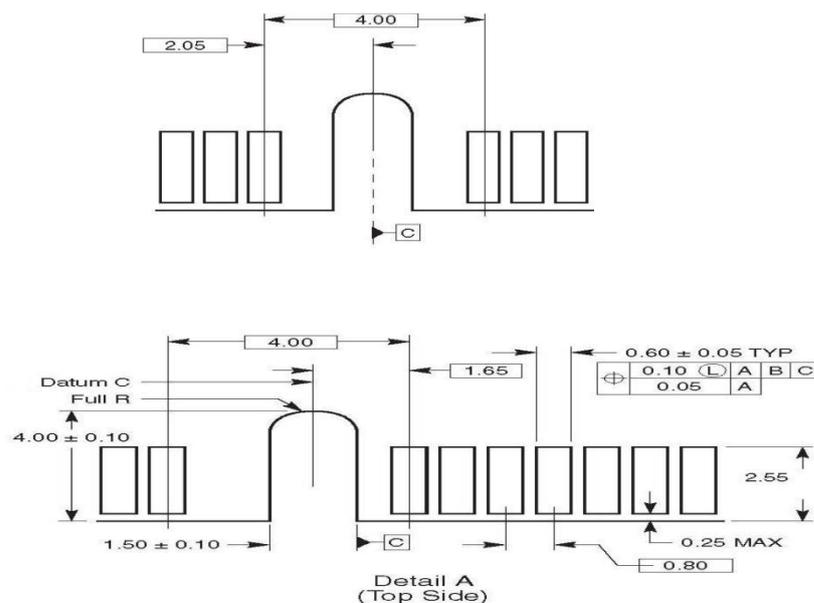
Mini PCIE Top 和 Bottom 细节尺寸
